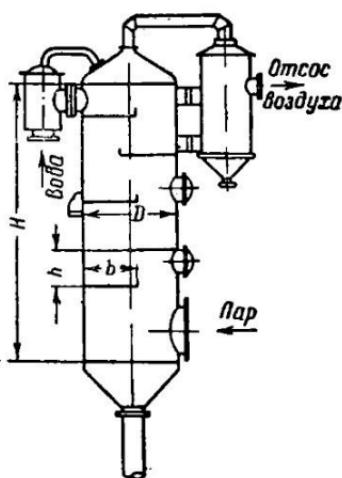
Барометрический конденсатор с сегментными полками.
